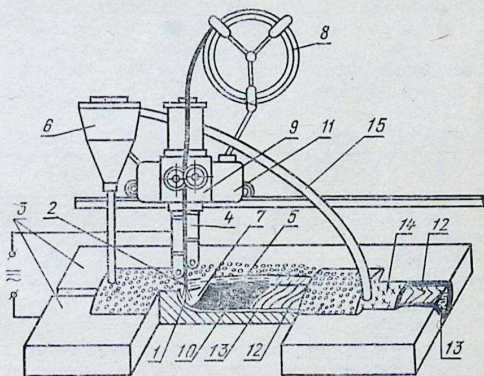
Схема автоматической сварки под слоем флюса:
